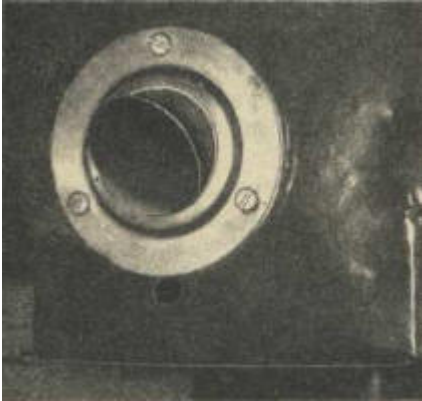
Mit drei Blechschrauben befestigtes Schauglas am Wärmetauscher
